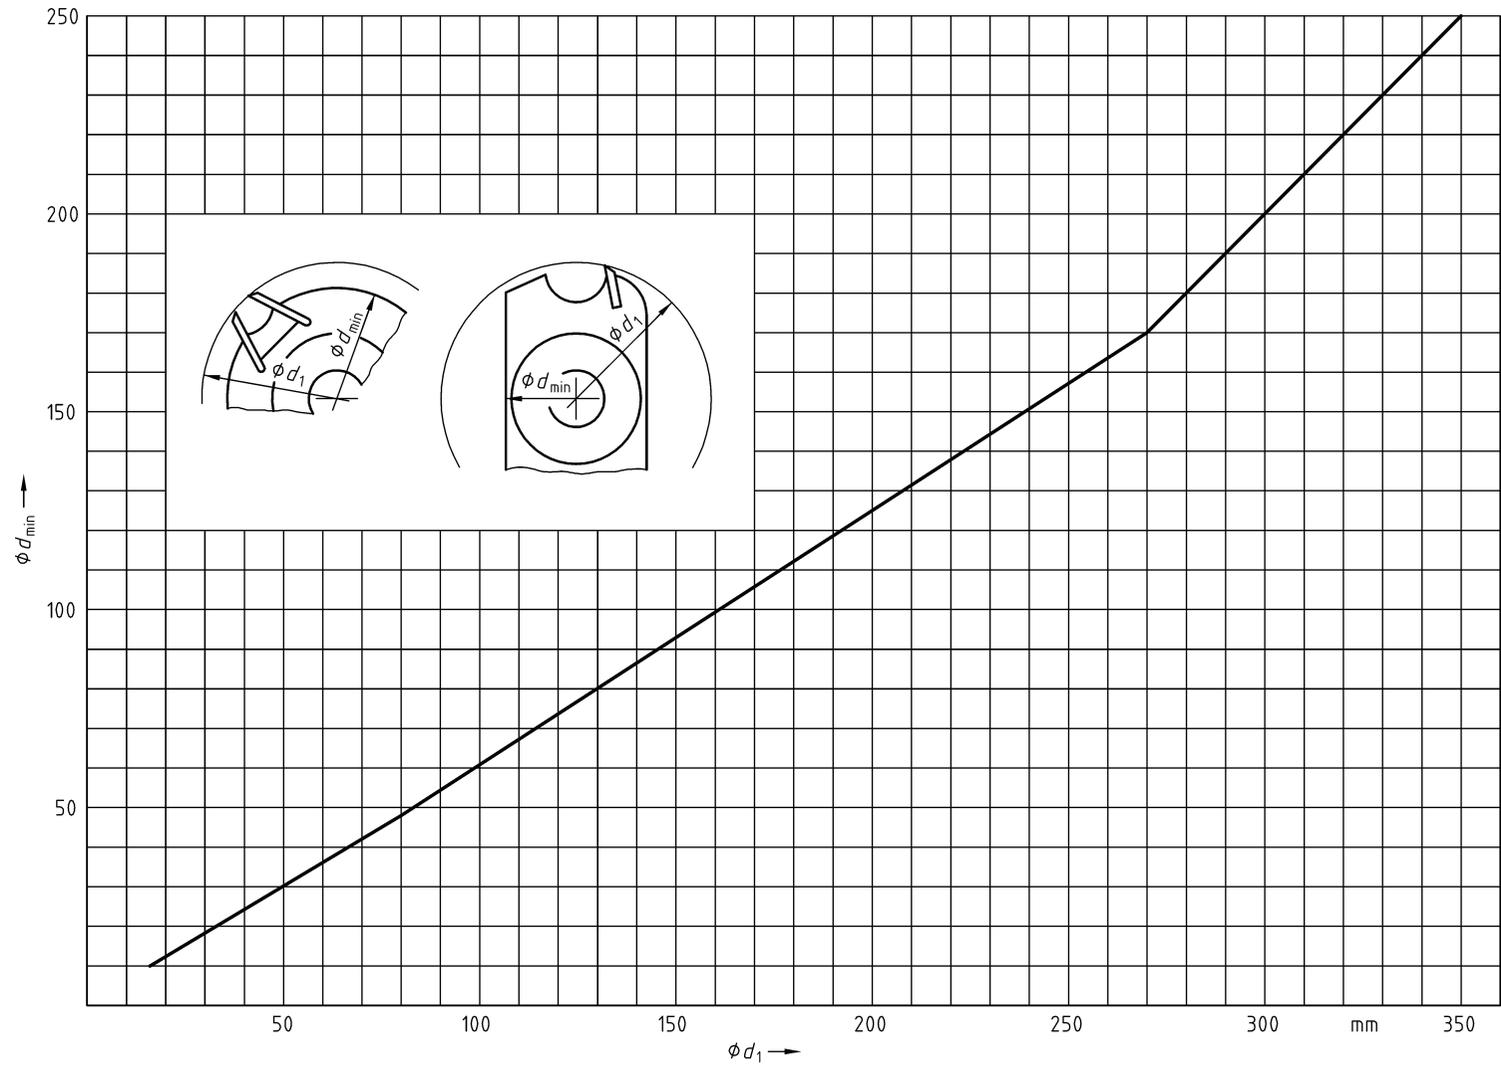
Mindestdurchmesser des Körpers  $d_{min}$  für Nichtrundform-Werkzeuge
